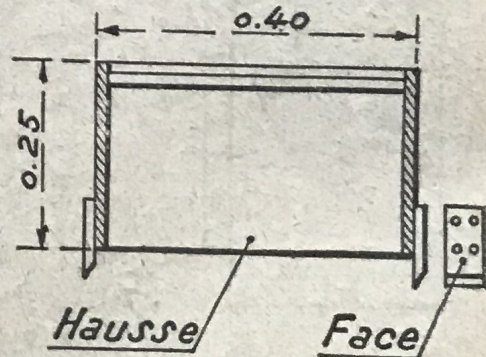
Hausse, ou magasin à miel, vu en coupe sur le côté; taquet de fixation vu de face.
